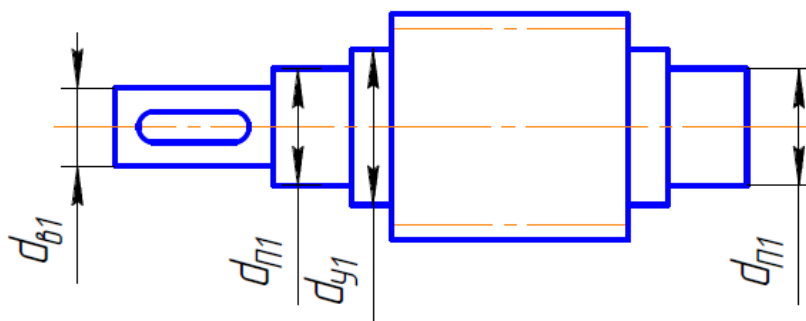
Типова конструкція швидкохідного валу редуктора
